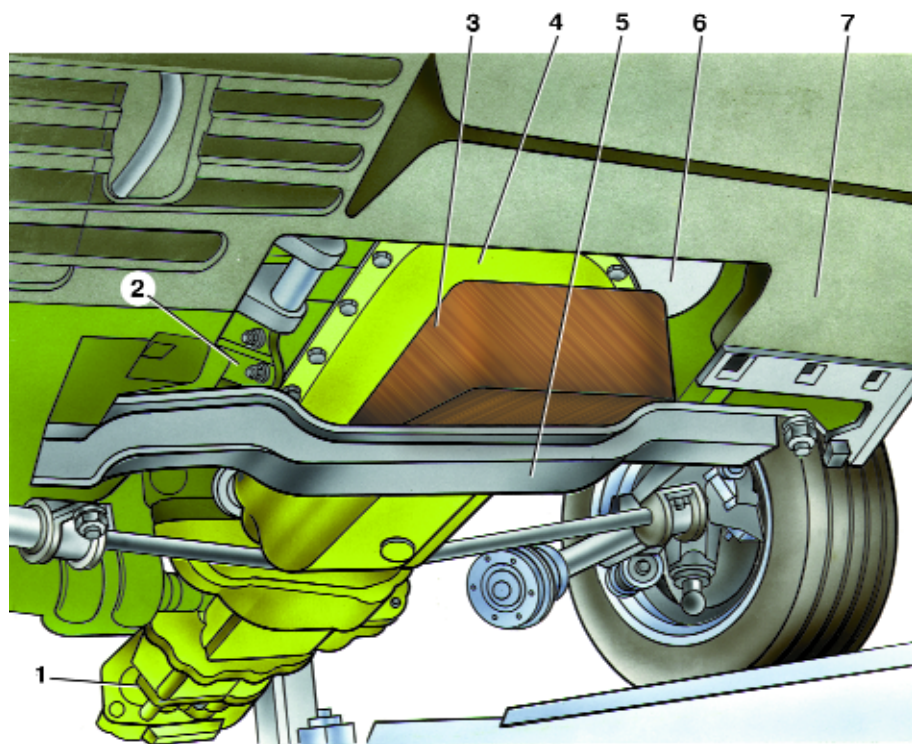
Вывешивание силового агрегата на передних опорах: 1 – задняя часть коробки передач; 2 – передняя опора; 3 – деревянный клин; 4 – поддон двигателя; 5 – поперечина; 6 – место расположения съемного пластмассового грязеотражательного щитка поддона двигателя; 7 – передний буфер
